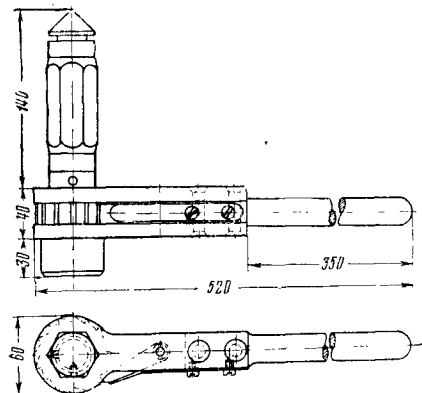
Рельсоверлильный станок ЦУМЗ
